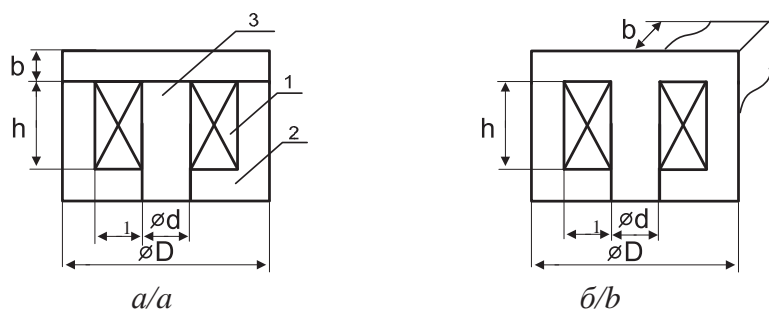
Конструкция броневых ЭМУ: а) с цилиндрическим якорем и корпусом; б) с цилиндрическим якорем и корпусом в виде скобы
